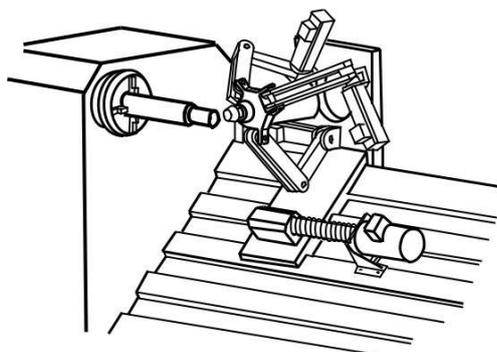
Токарный станок с МПС по пат. ФРГ №1994092
